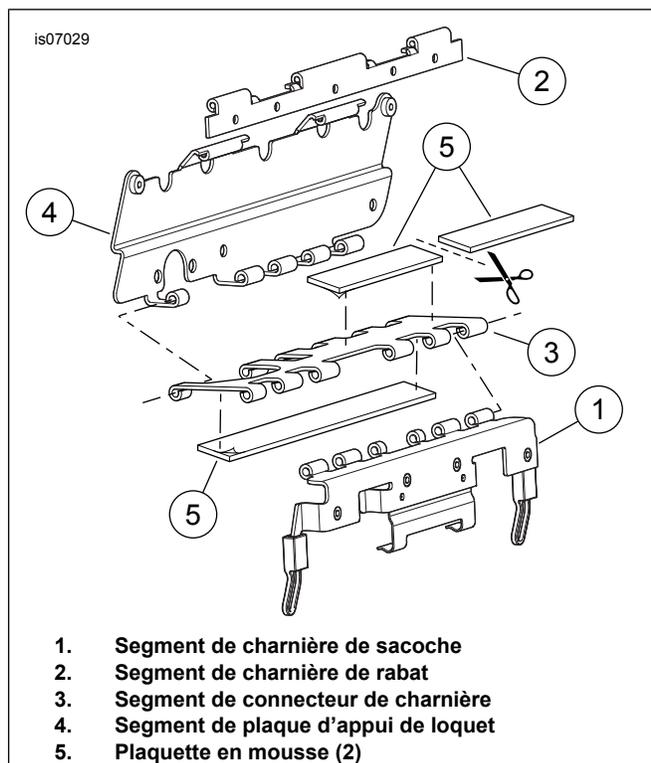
Installer les coussinets en mousse sur la charnière du loquet de sacoche (côté gauche illustré)
